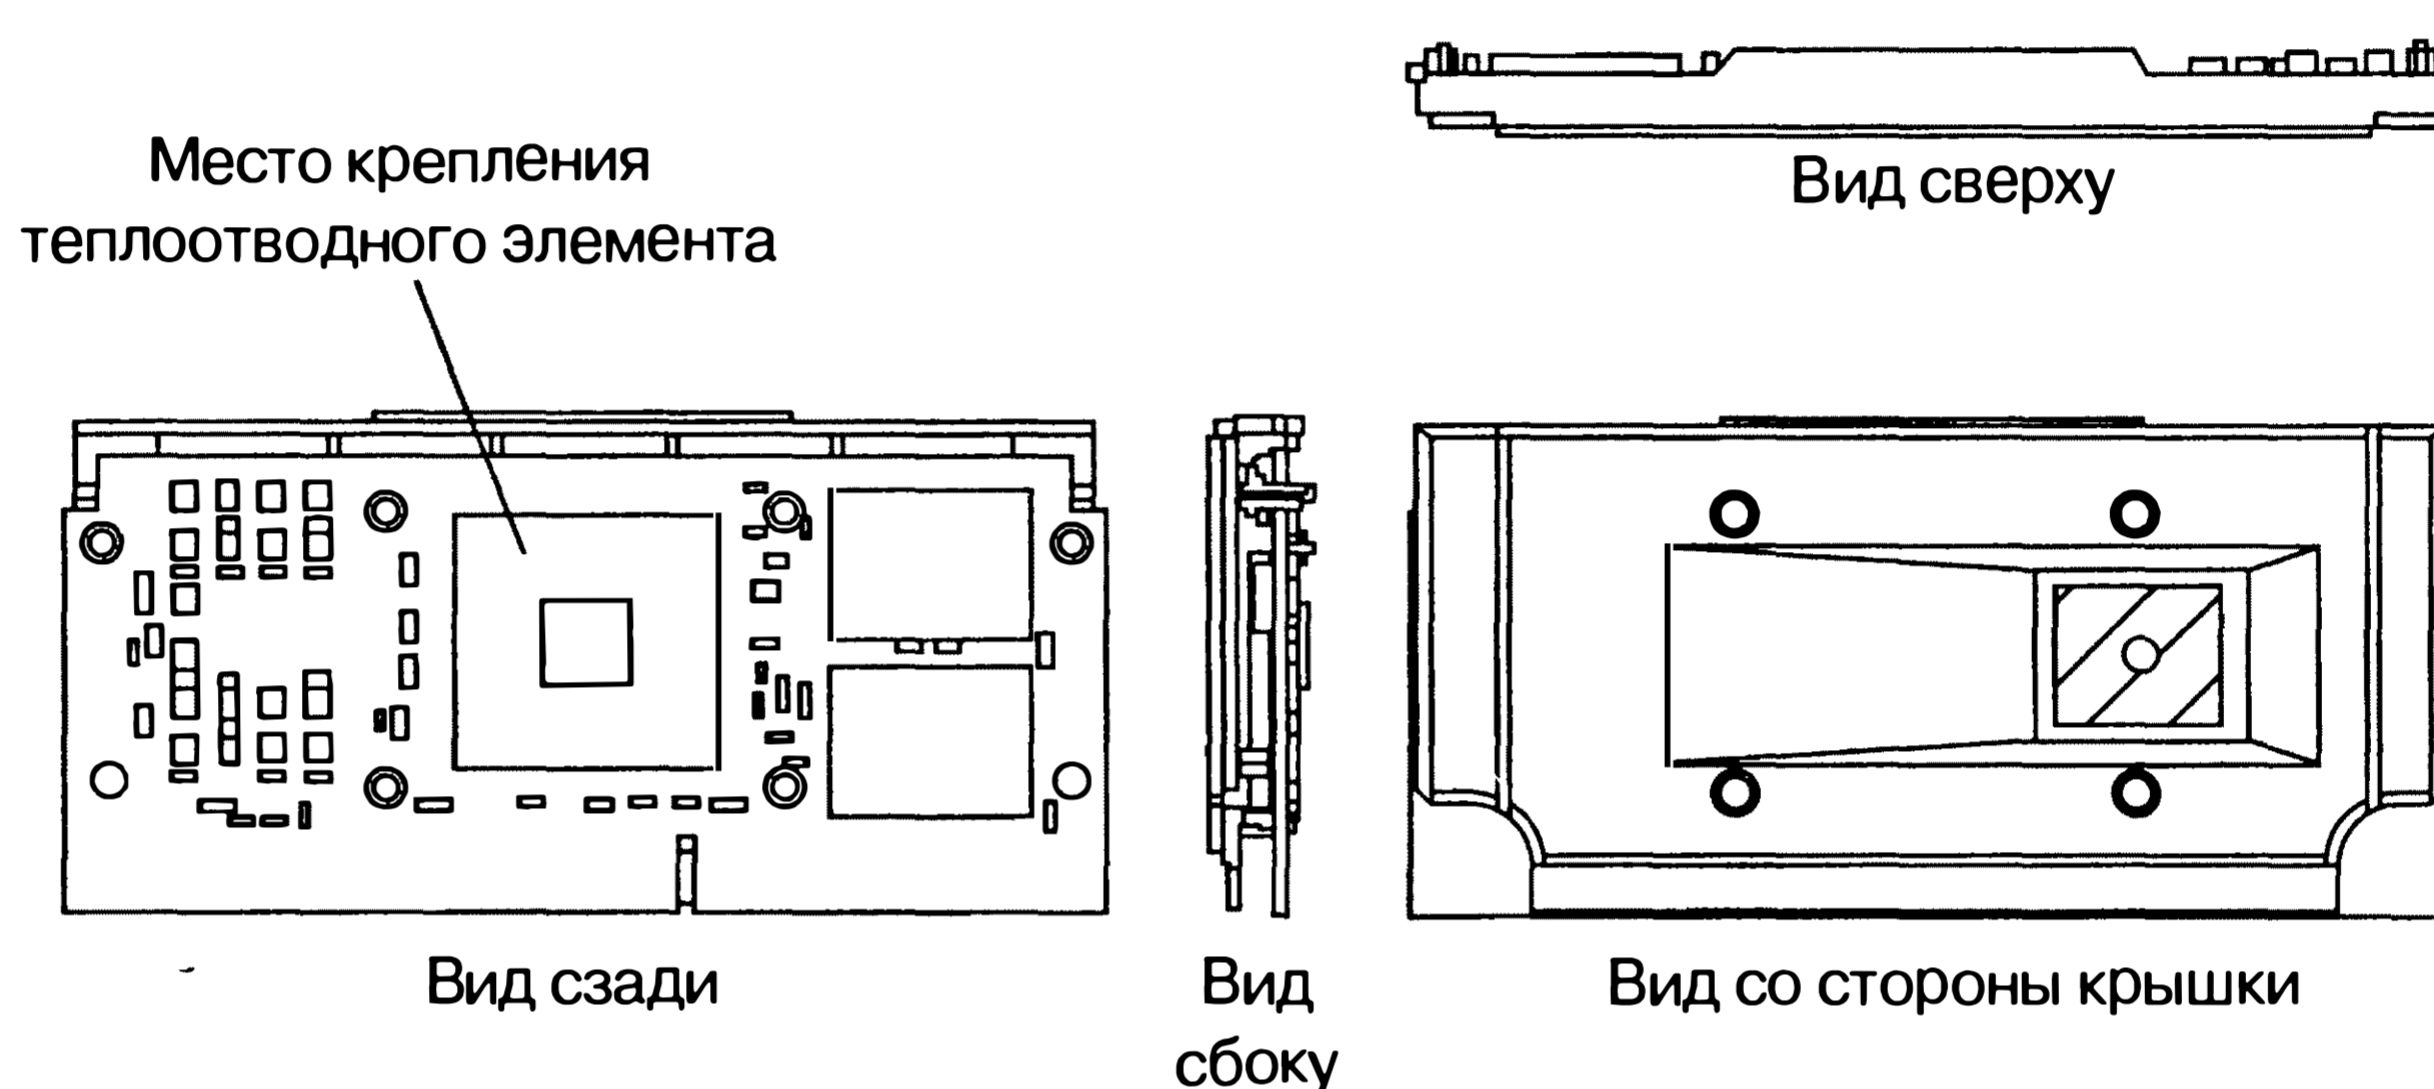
Корпус SECC2 процессоров Pentium II/III
